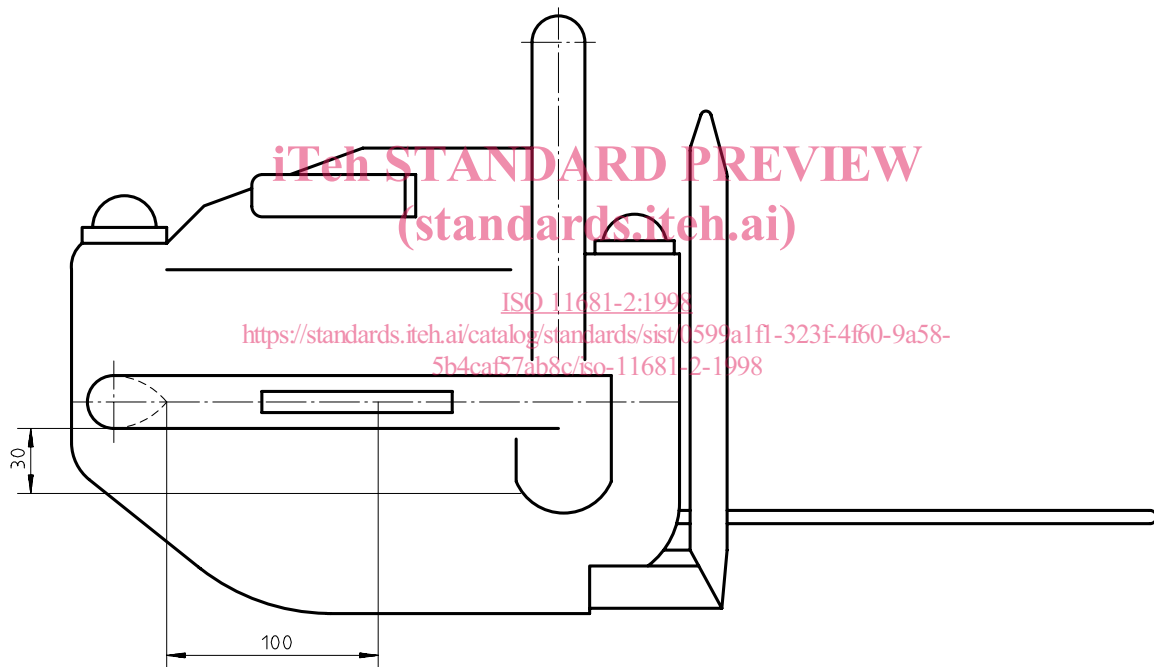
Dimensions minimales de la protection au niveau de la poignée arrière
